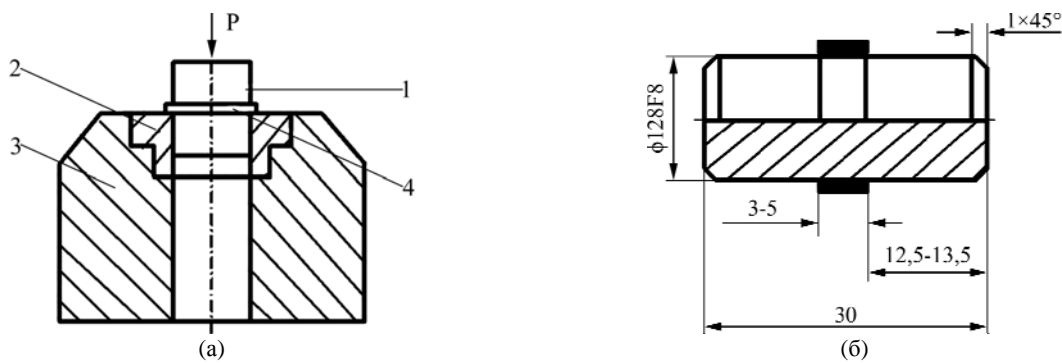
Схема испытания (а) образцов (б) на прочность сцепления при сдвиге: 1 – образец; 2 – матрица; 3 – корпус; 4 – слой металлопокрытия.
